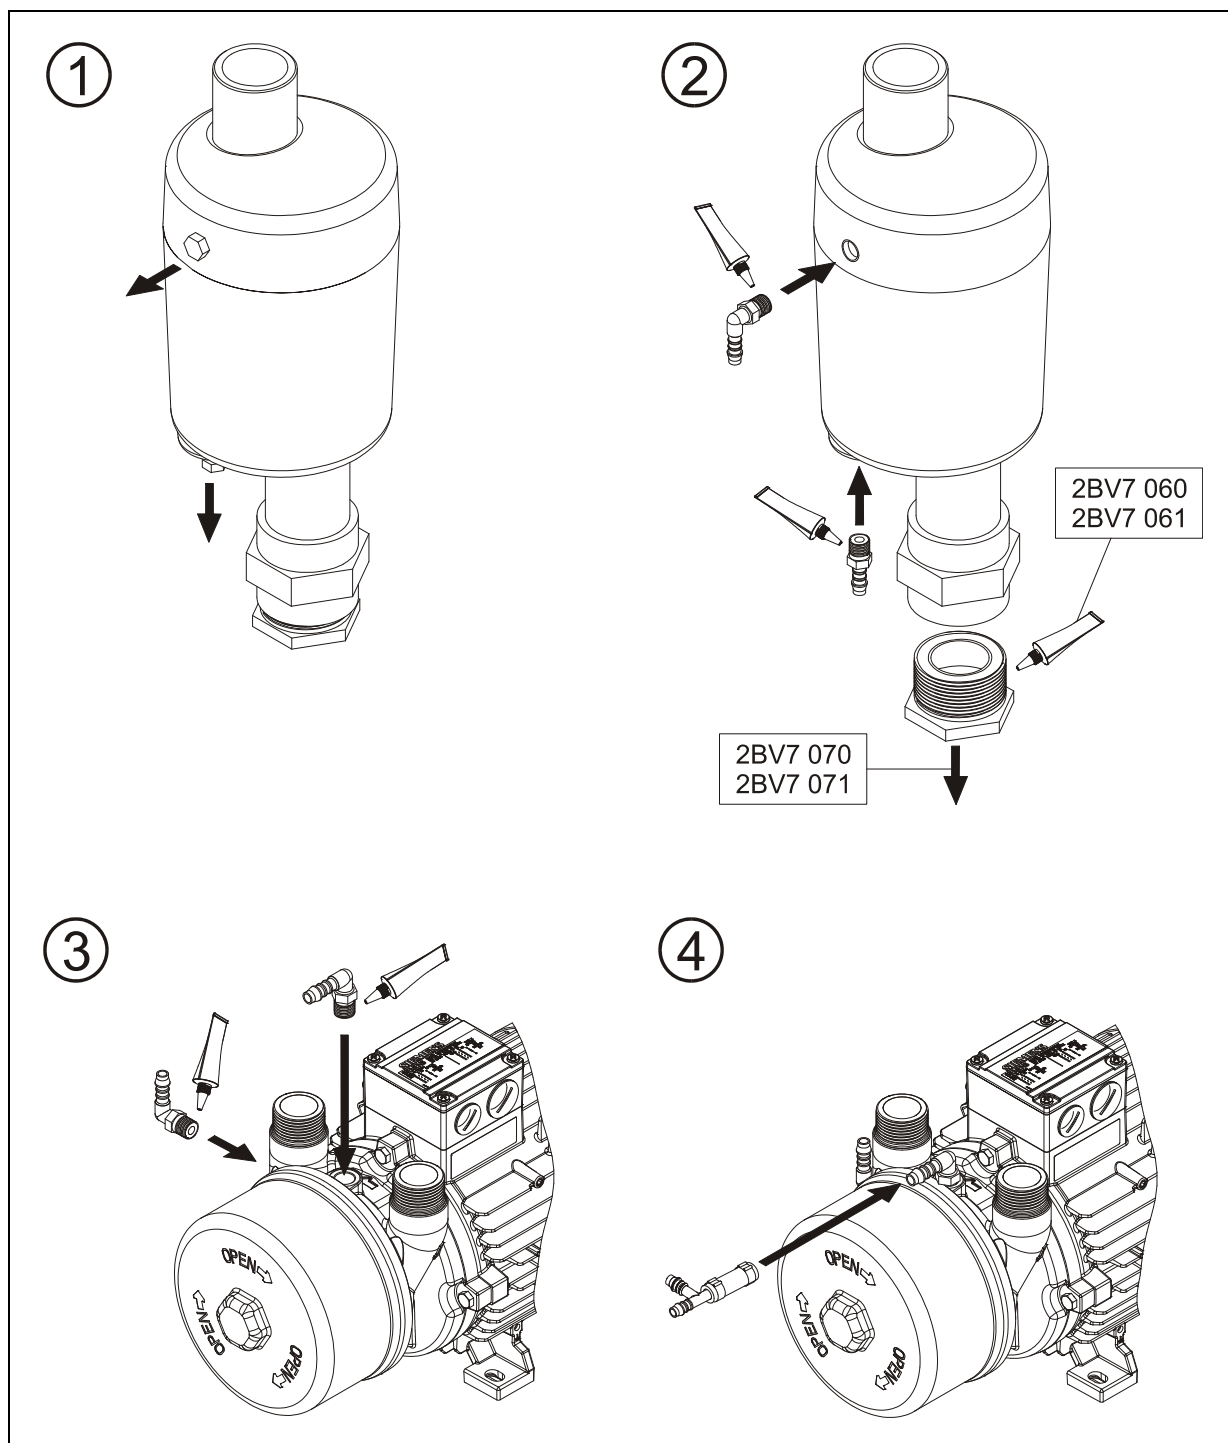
Montaggio del separatore di liquidi, parte 1 di 2
